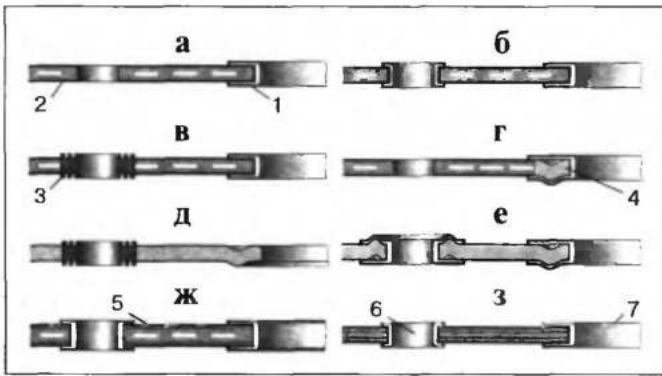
Основные типы прокладок головок цилиндров: а — стандартная конструкция с окантовкой цилиндров; б — с дополнительной окантовкой каналов смазки и/или охлаждения; в — с фасонной резиновой вставкой; г — комбинированная прокладка с дополнительным стальным кольцом у цилиндров; д — стальная прокладка без окантовки у цилиндров; е — то же, с окантовкой; ж — комбинированная многослойная прокладка с мягким материалом; з — комбинированная многослойная стальная прокладка; 1 — окантовка; 2 — основа (мягкий материал); 3 — фасонная резиновая вставка; 4 — дополнительное стальное кольцо; 5 — стальной лист; 6 — отверстие масляного канала; 7 — отверстие цилиндра
